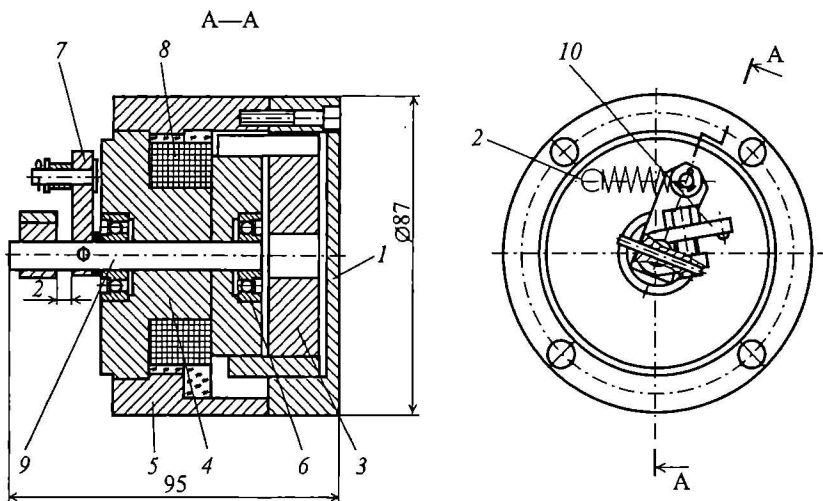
Поворотный электромагнит для исполнительного устройства ЭГУ106М: 1 — крышка; 2 — пружина; 3 — яркость; 4 — магнитопровод; 5 — корпус; 6 — подшипник; 7 — рычаг пружины; 8 — катушка электромагнита; 9 — вал; 10 — упорный рычаг
